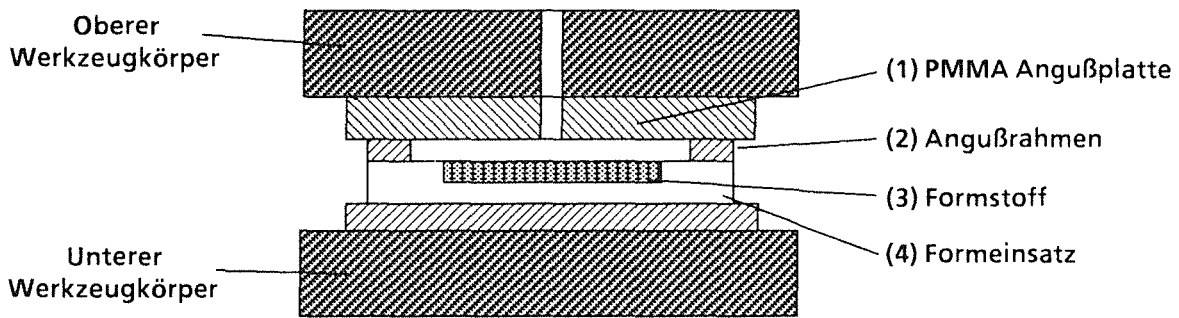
Schematischer Aufbau des Werkzeuges "W4" zum Aufschießen einer separat gefertigten Trägerplatte auf einen mit Formstoff befüllten Formeinsatz
